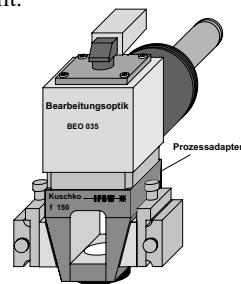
Trumpf Bearbeitungsoptik mit Prozessadapter für Nd:YAG-Schweißversuche.
